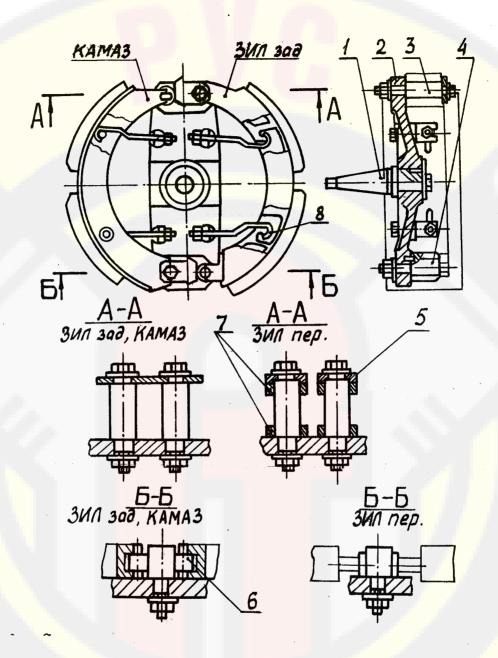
Приспособление для обточки тормозных Накладок автомобилей ЗИЛ, КАМАЗ.
